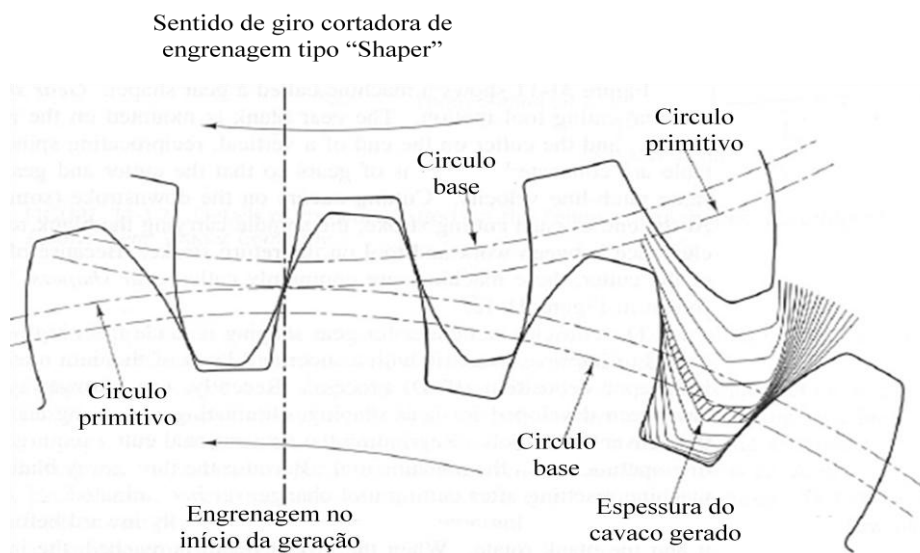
Movimentos entre ferramenta e engrenagem na geração dos dentes (Shigley, 1984)
